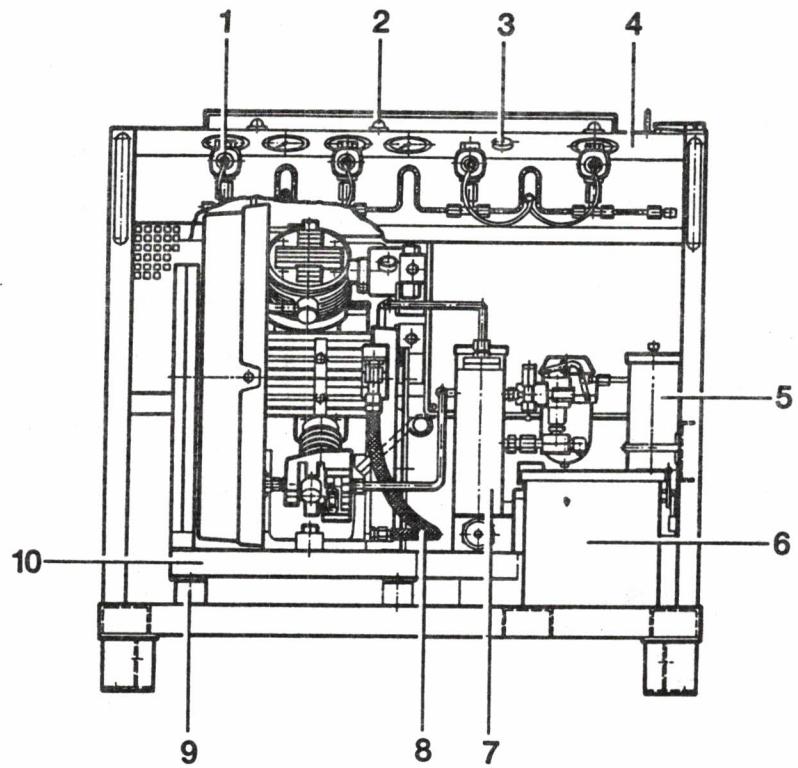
Drucklufterzeuger (EliMot), Seitenansicht, links
